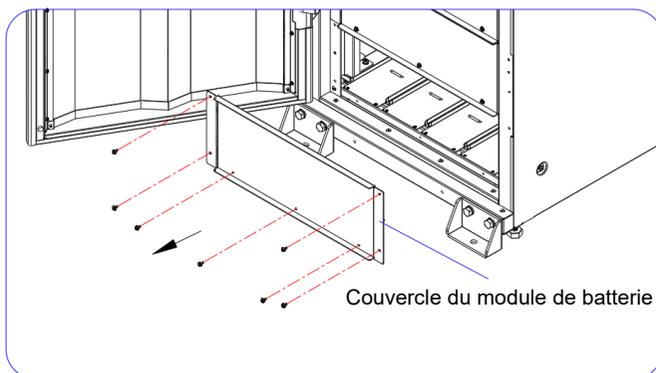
Panneau arrière\_Emplacement des vis)
